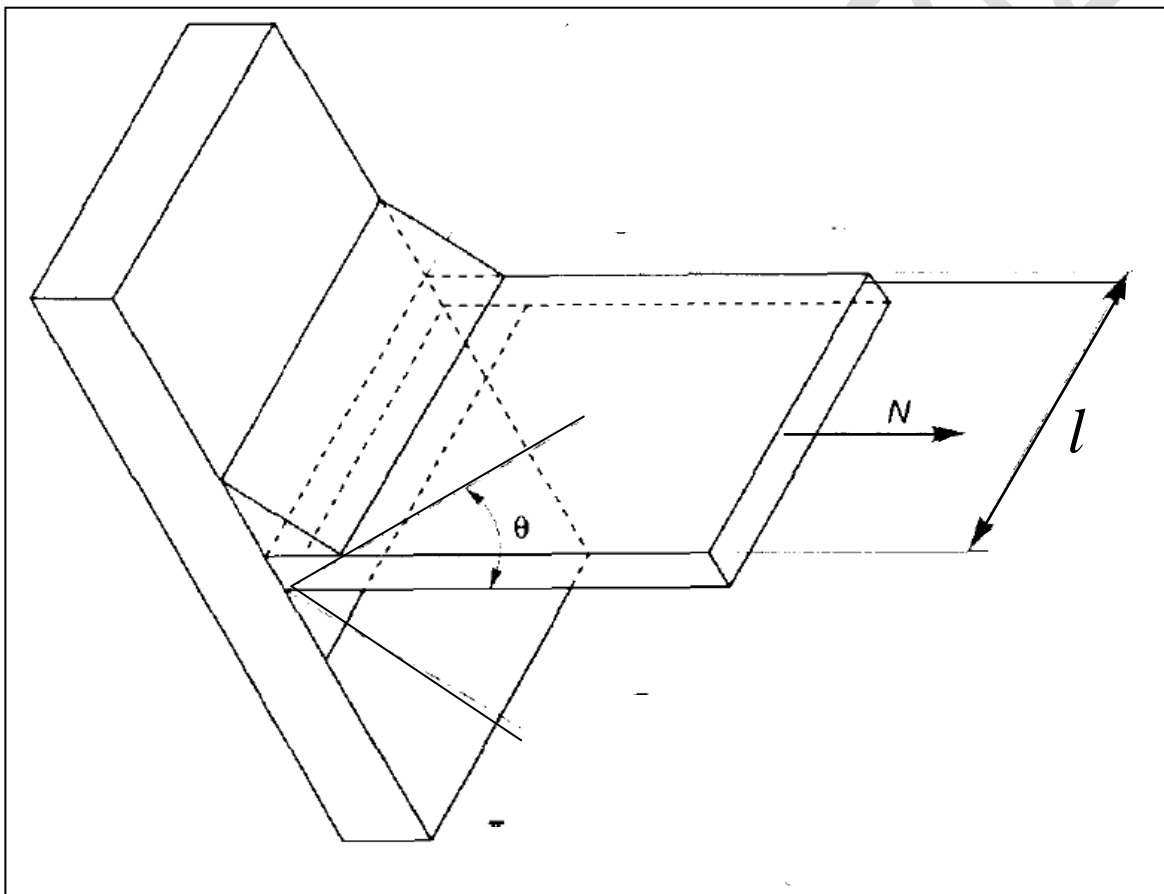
Cordons de soudures reliant des pièces obliques
